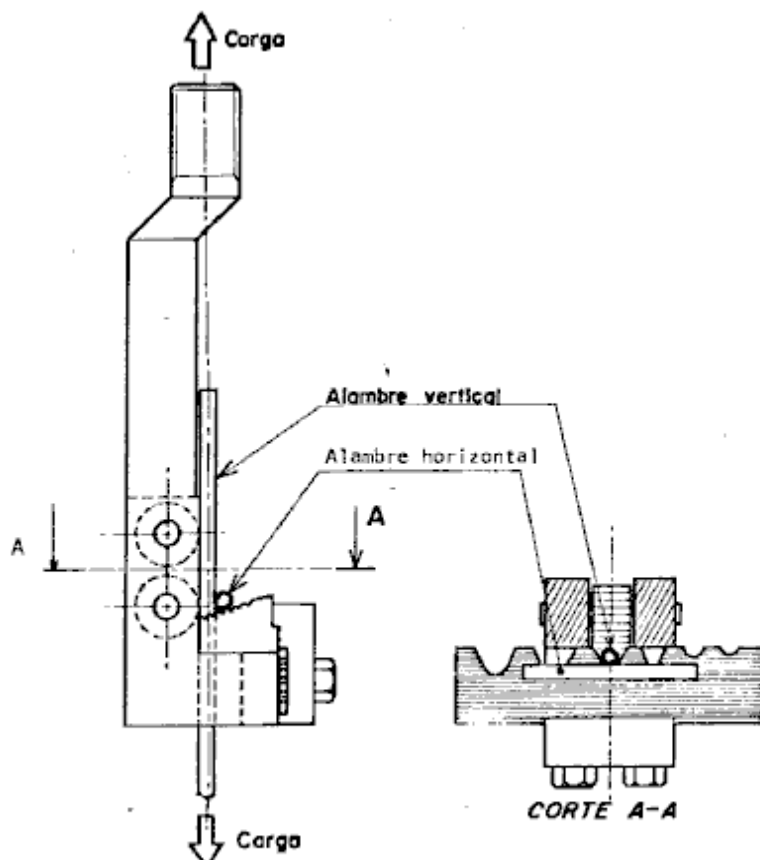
Dispositivo de prueba de soldadura para mallas de alambre soldado.
